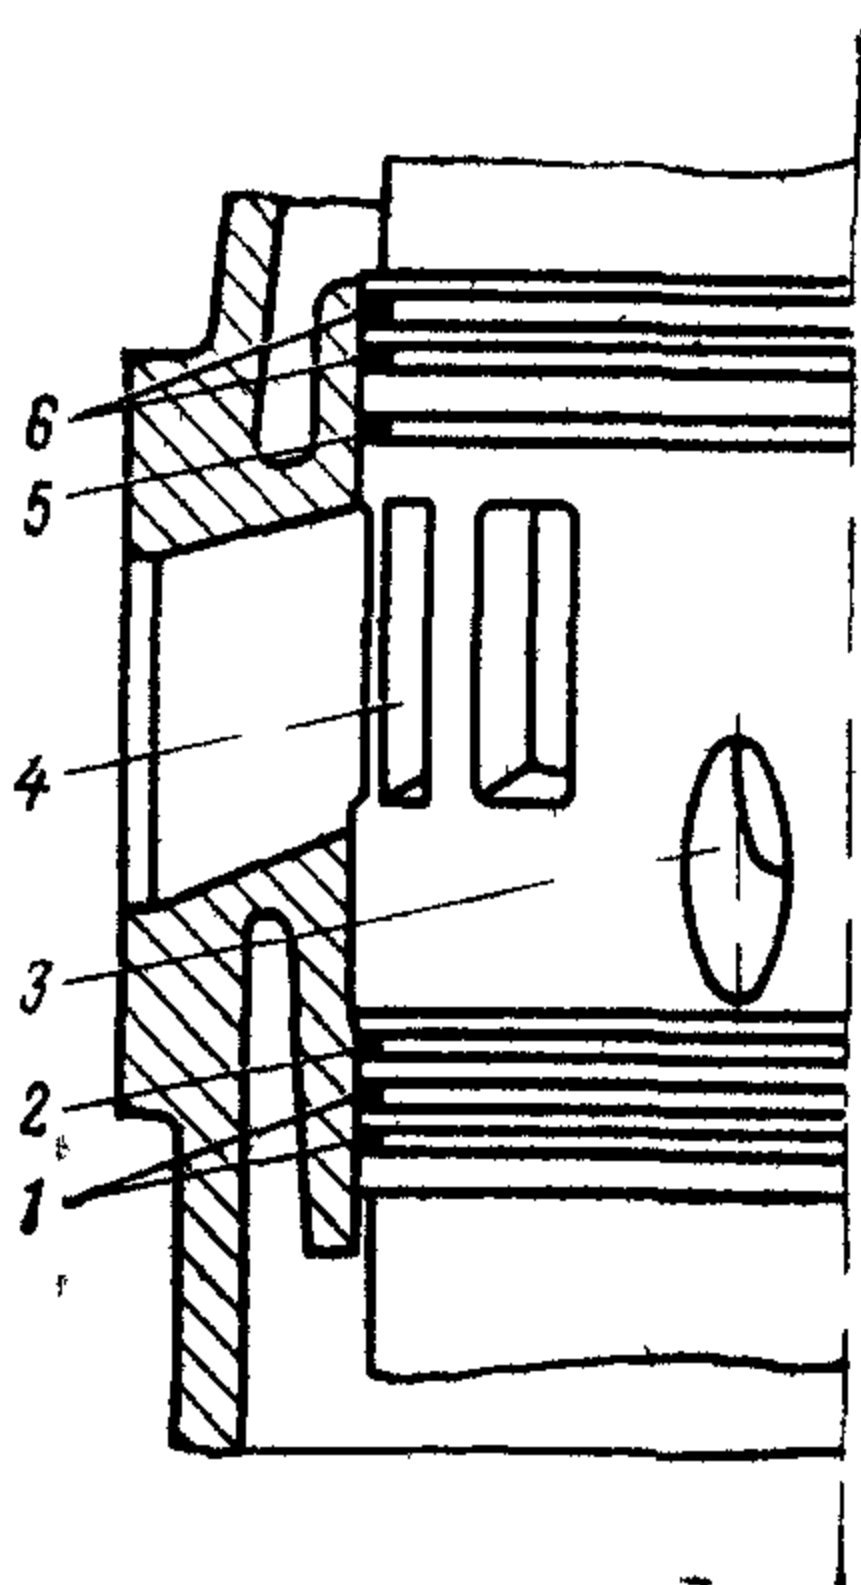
Способ уплотнения втулки цилиндра двухтактного двигателя
